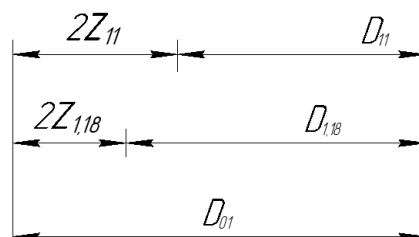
Размерная цепь для расчета размера $\varnothing 45h12$, обработка наружной поверхности.
